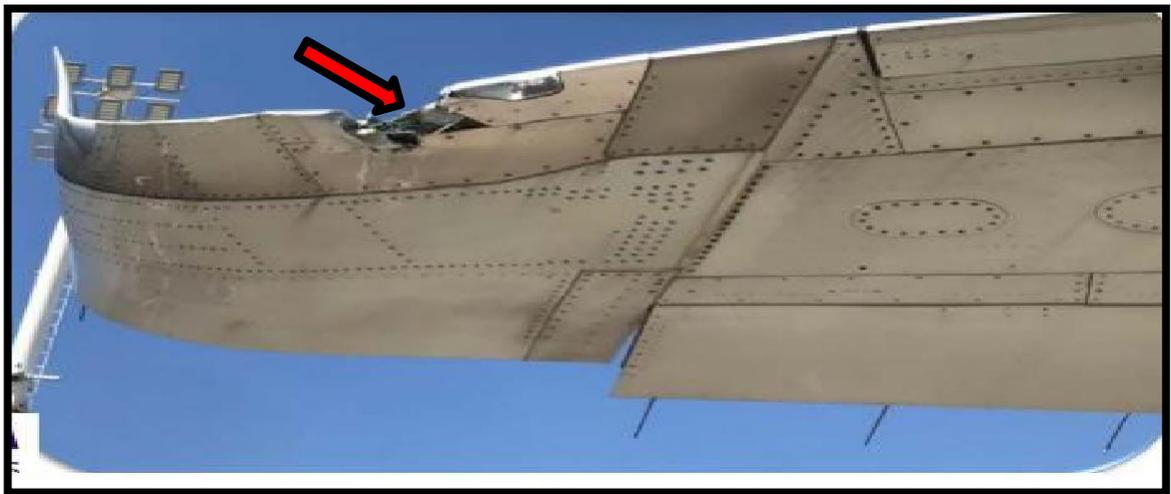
y N°3: Vista del Wingtip-Fence dañado del ala izquierda y una punta de este, en la losa de estacionamiento.
